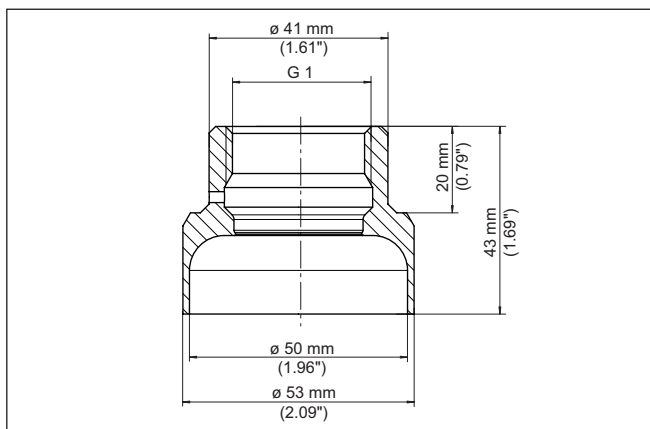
Dimensions raccord à souder direct pour montage sur tube G1 - Joint torique
